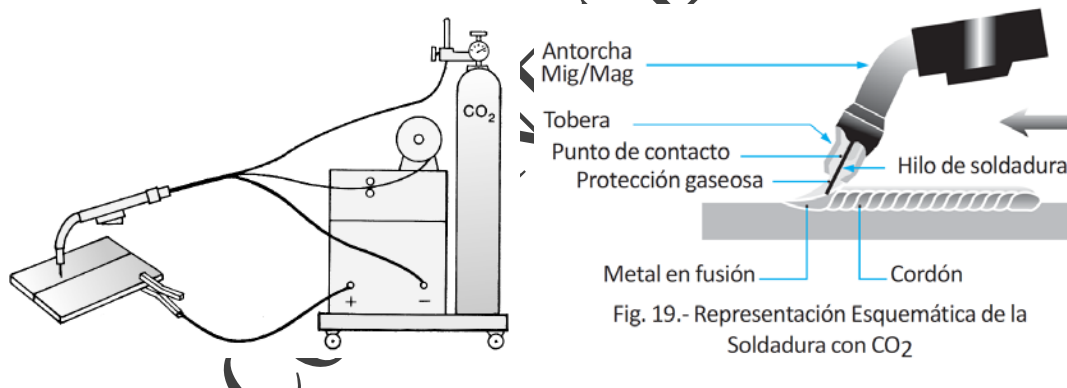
Representación Esquemática de la Soldadura con CO₂
